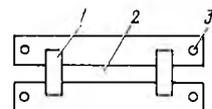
Приспособление для снятия спирали проволоки с планки: 1 — косынка (2 шт.); 2 — паз для продвижения планки; 3 — отверстие для крепления приспособления (4 шт.)
